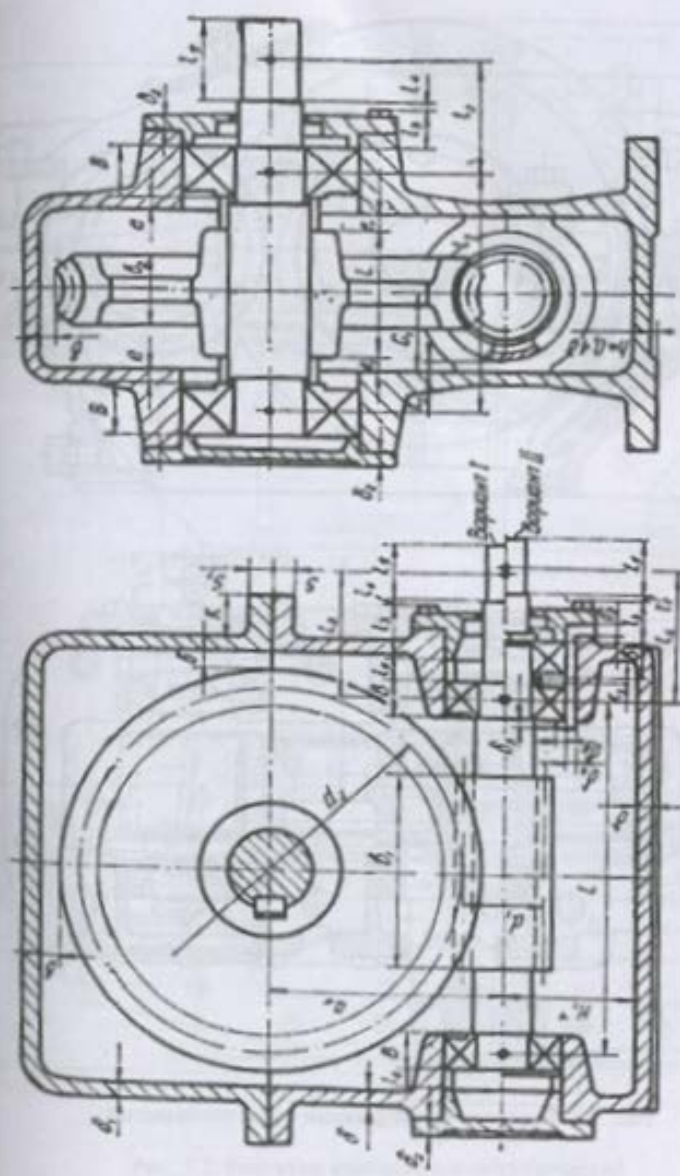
Компонувальний ескіз черв'ячного редуктора
